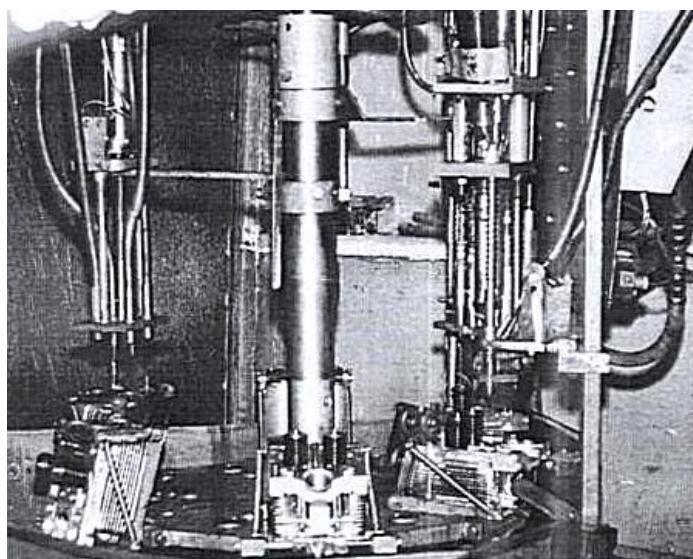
Двух- и четырехшпindleвое завинчивающее устройство для автоматизированного переналаживаемого комплекса сборки головки цилиндра тракторного двигателя
